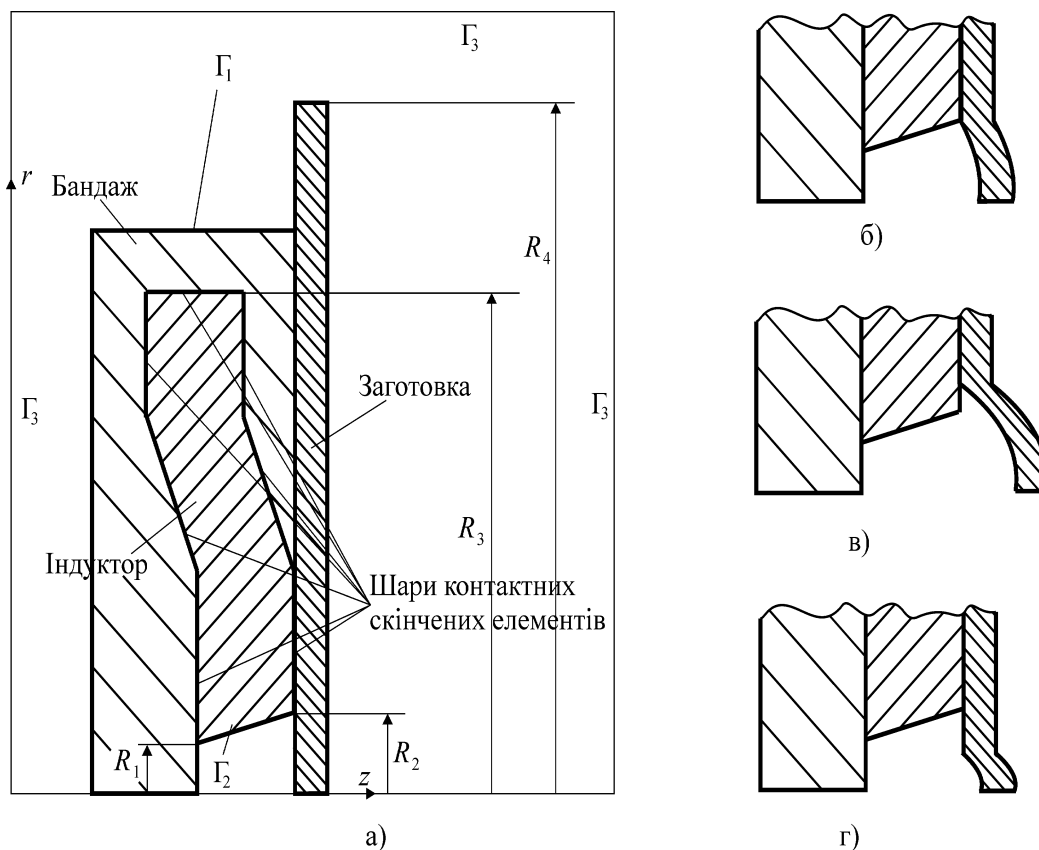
Розрахункова схема індуктора разом із діелектричним бандажем та заготовки із різними варіантами вм'ятини
